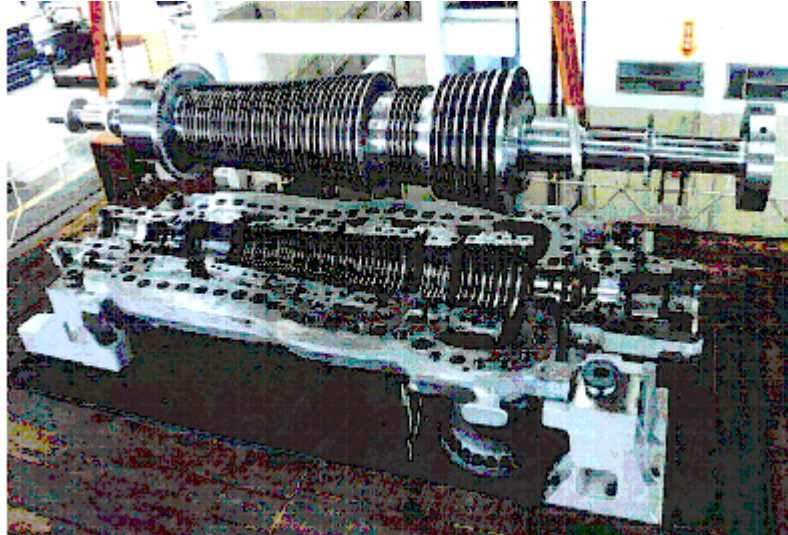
Turbina a vapor multi-estágio –vista do rotor
